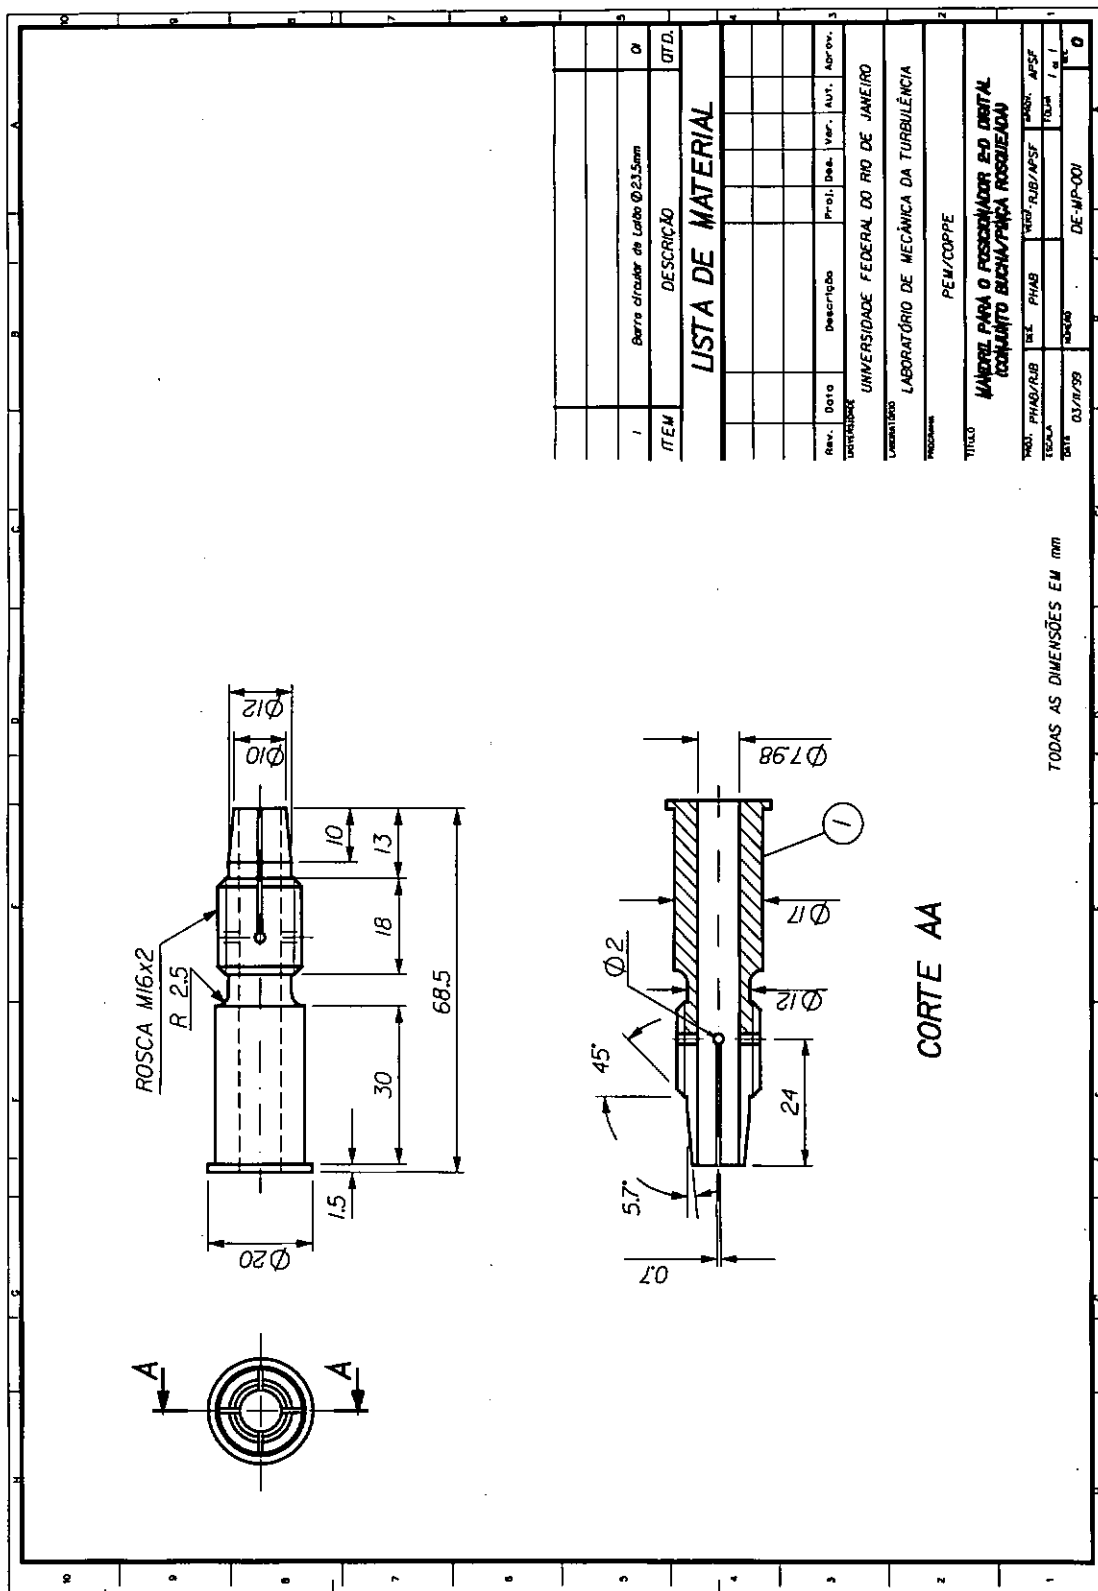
Parte do desenho técnico do conjunto bucha-mandrill projetado para o posicionador 2D utilizado nos experimentos (peça: bucha/pinça rosqueada).
